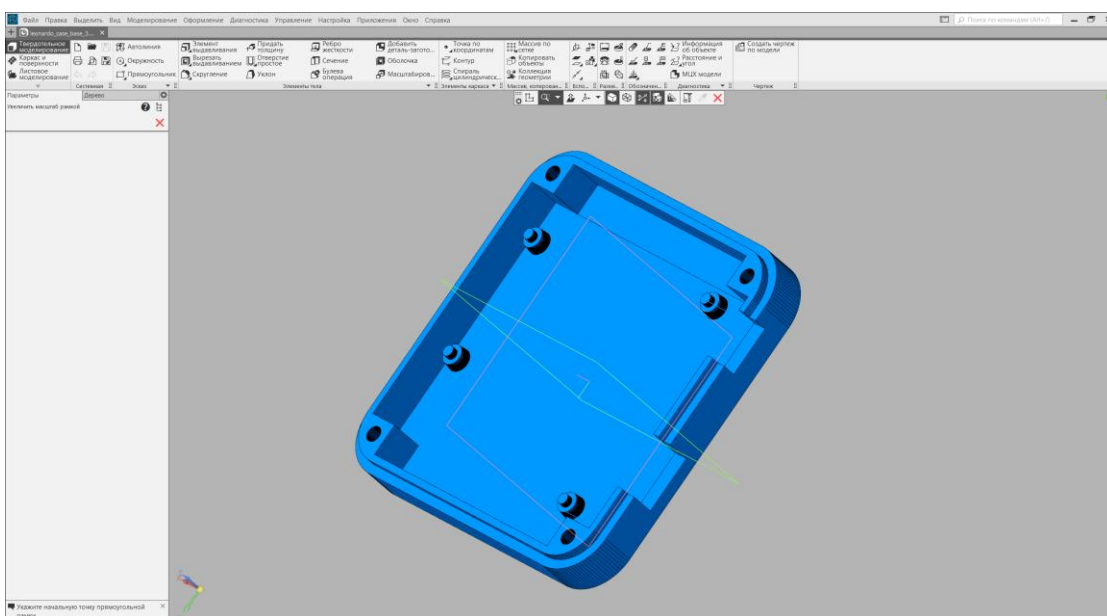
Разработка и размещение модели корпуса РЭА
